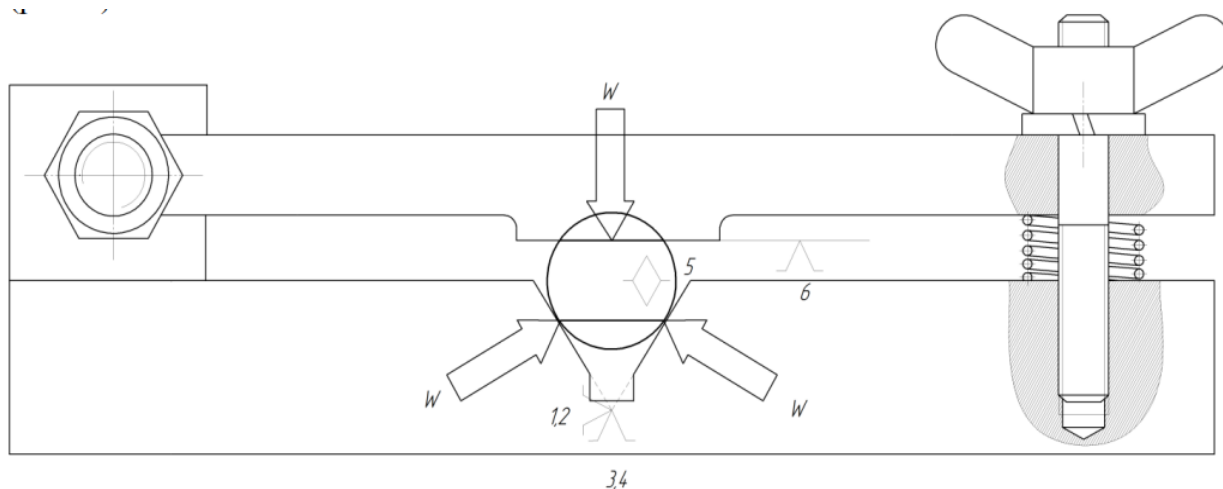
Принципова схема затискання заготовки в пристосуванні із зазначенням місць прикладання сили затиску
